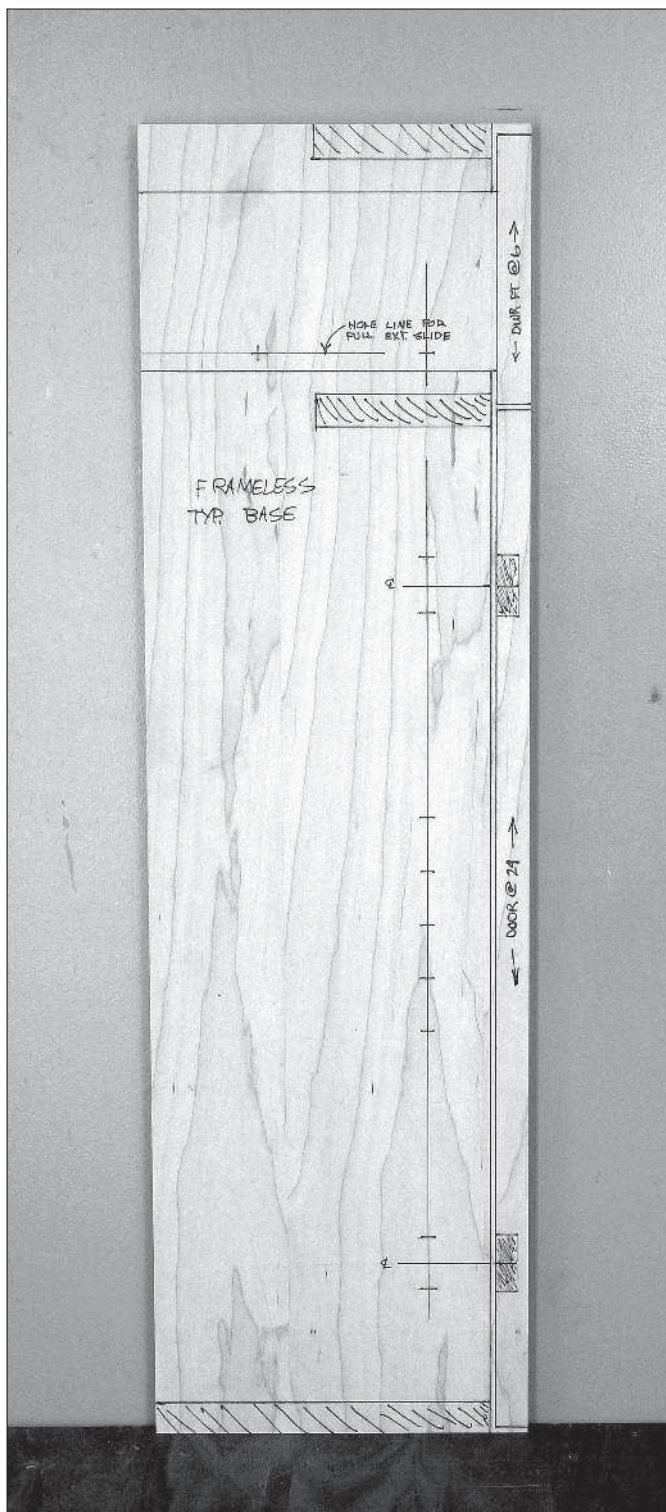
Заготовка европейской системы – Разметка заготовки для щитового шкафа показывает расположение и размеры всех ее участков и монтажных отверстий под фурнитуру для типового базового модуля.
